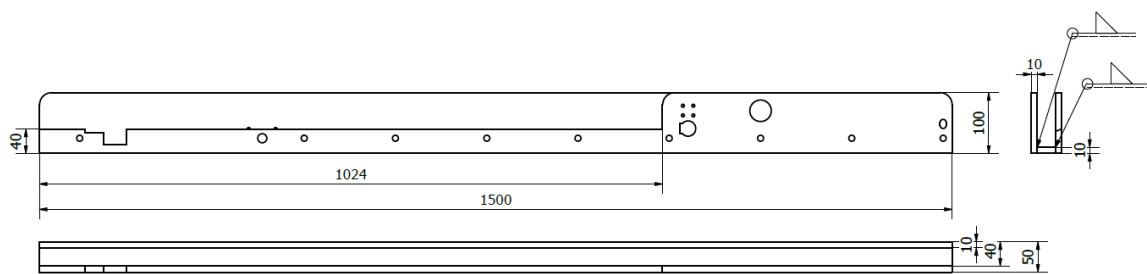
Esquema de soldadura da estrutura do caleiro do sistema de fornecimento, medidas em mm.
